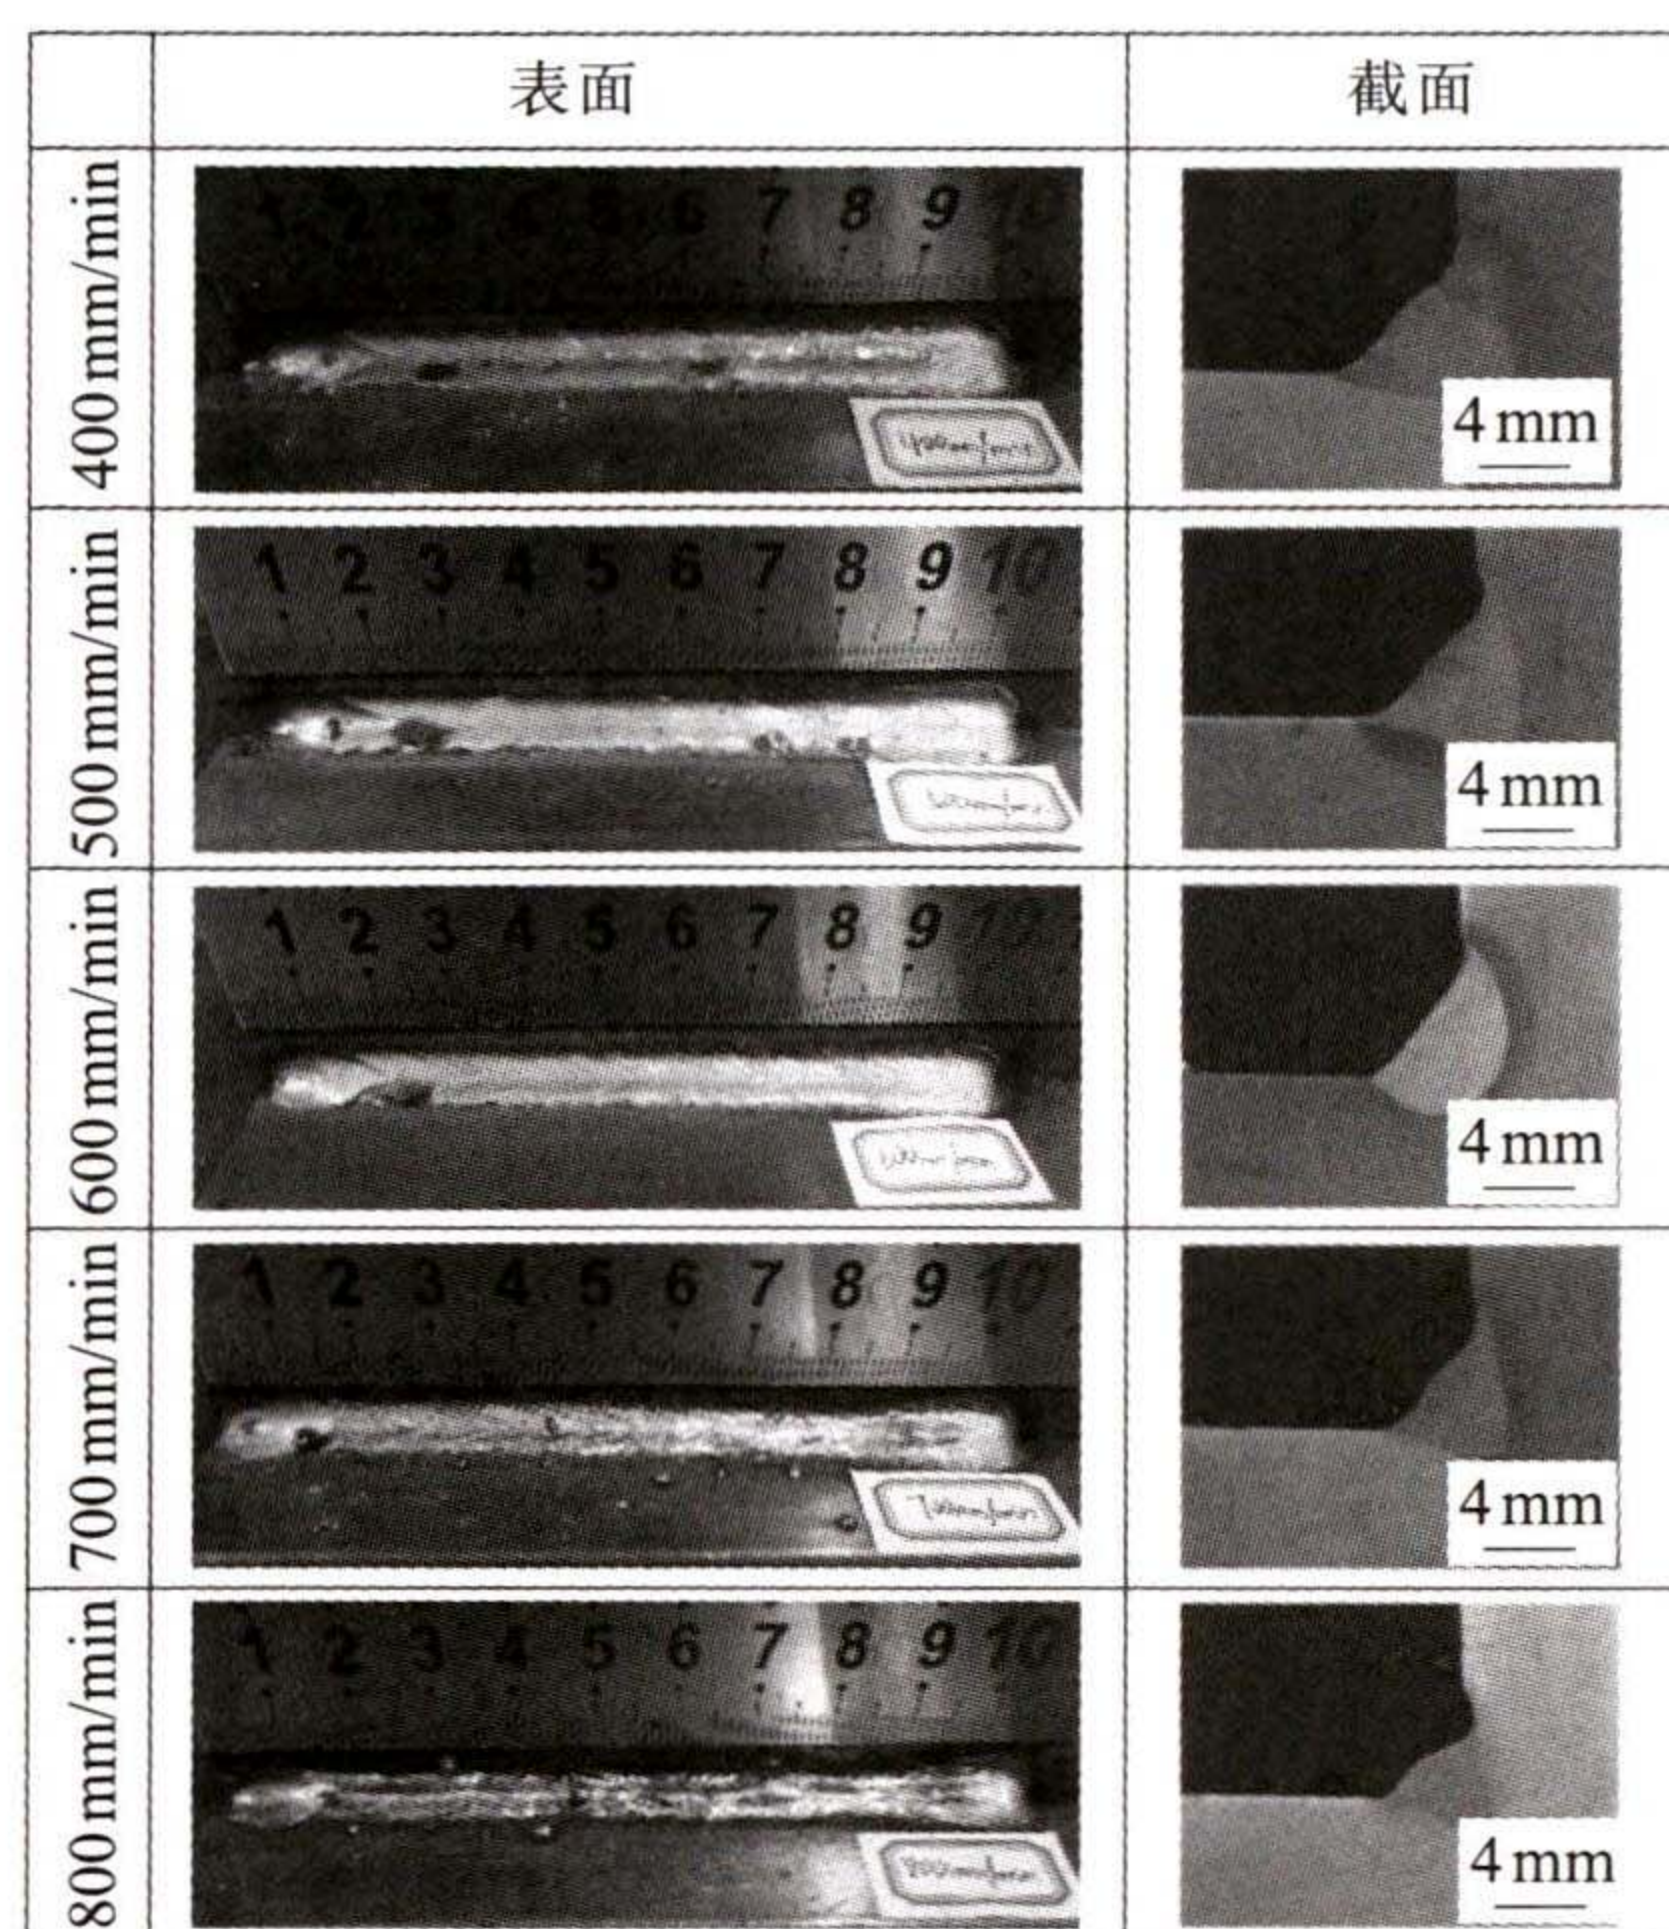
不同焊接速度下焊缝的表面和截面形貌
